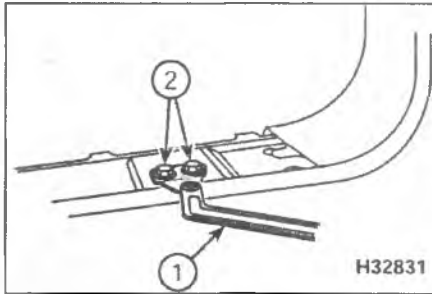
Выверните из бруса нижней обвязки багажного отделения два болта (2) крепления ограничителя открывания двери (1)
